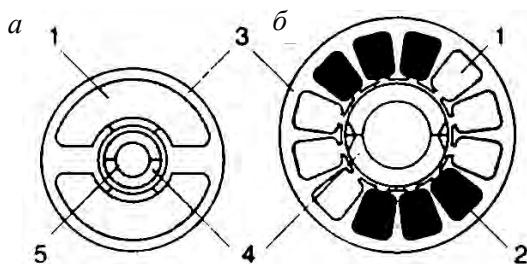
Электродинамический поворотный исполнительный механизм:
